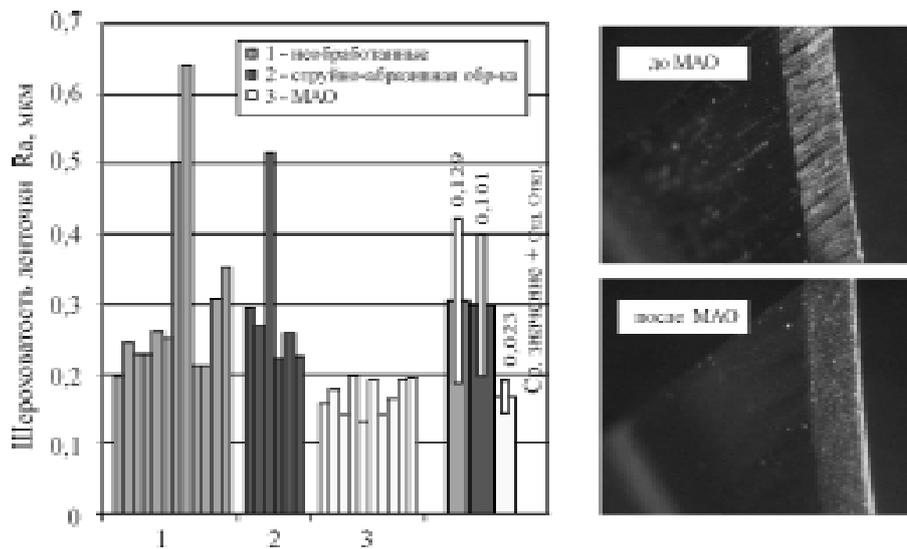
Влияние MAO и пескоструйной обработки на шероховатость калибрующей ленточки
